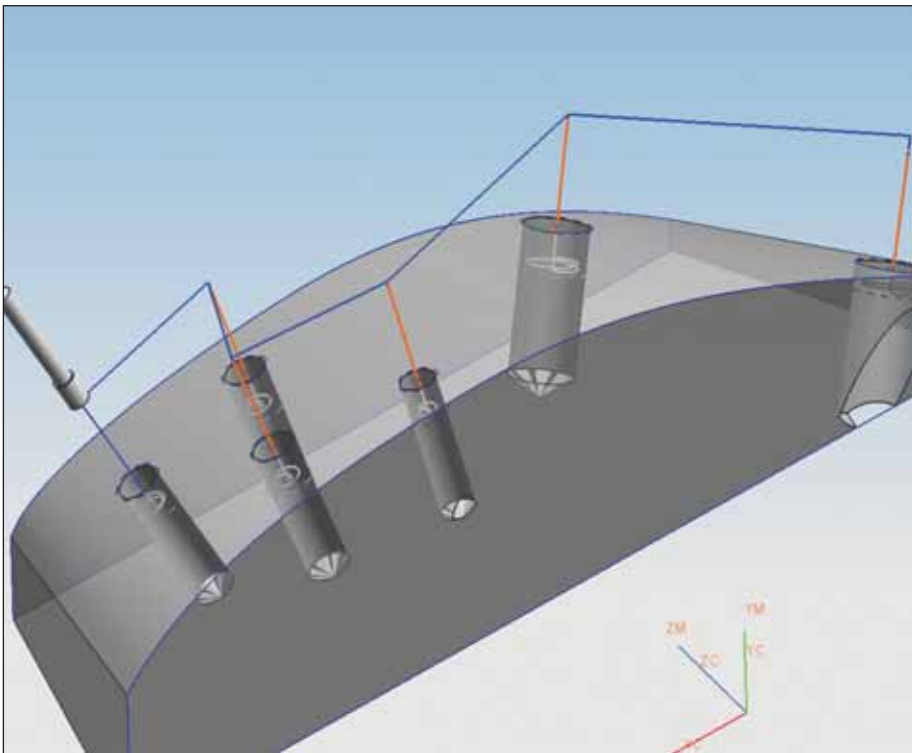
Резьбофрезерование нескольких отверстий на условной "теоретической" поверхности
